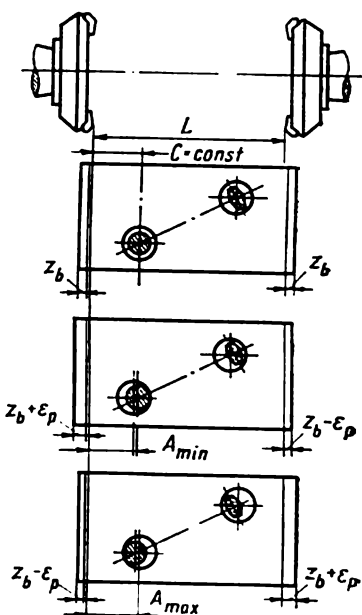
Positionnement d'une pièce de support d'après un plan et deux trous de tenue pratiqués dans ce plan
